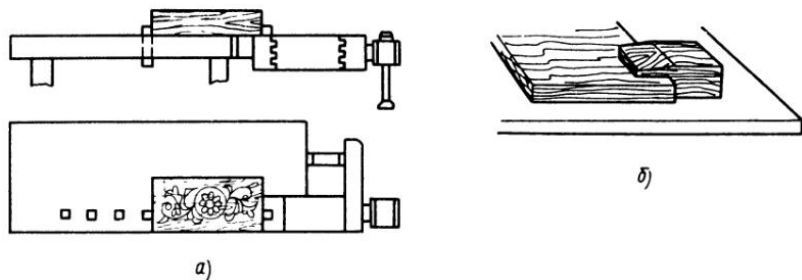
Закрепление заготовки для резьбы на верстаке:
